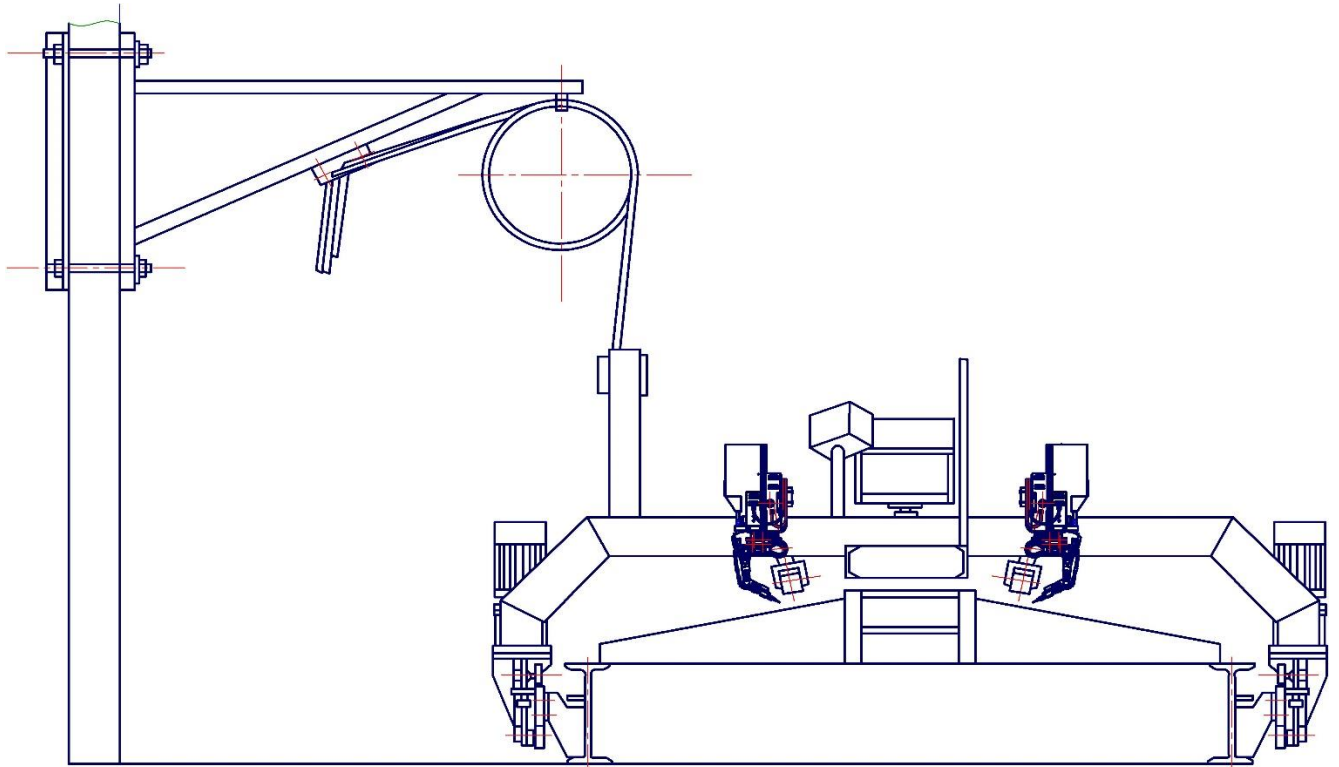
Схема зварювального порталу для виготовлення даху вагона
